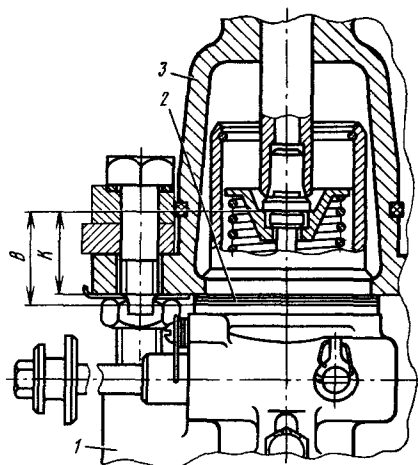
Определение толщины регулировочных прокладок под корпус топливного насоса дизеля типа Д100:
